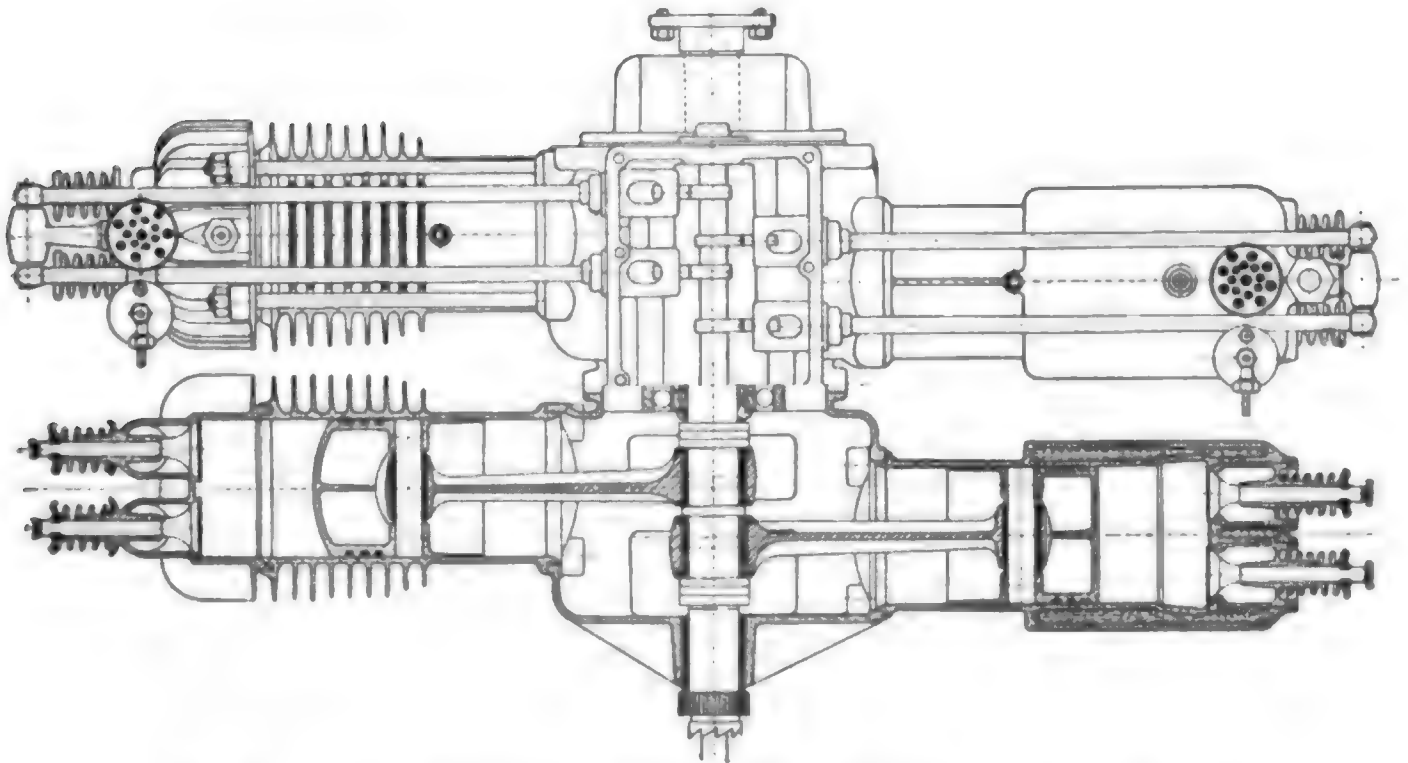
Zeichnung des Flugmotors von Escher & Co., Längsschnitt, bzw. Ansicht von oben.
